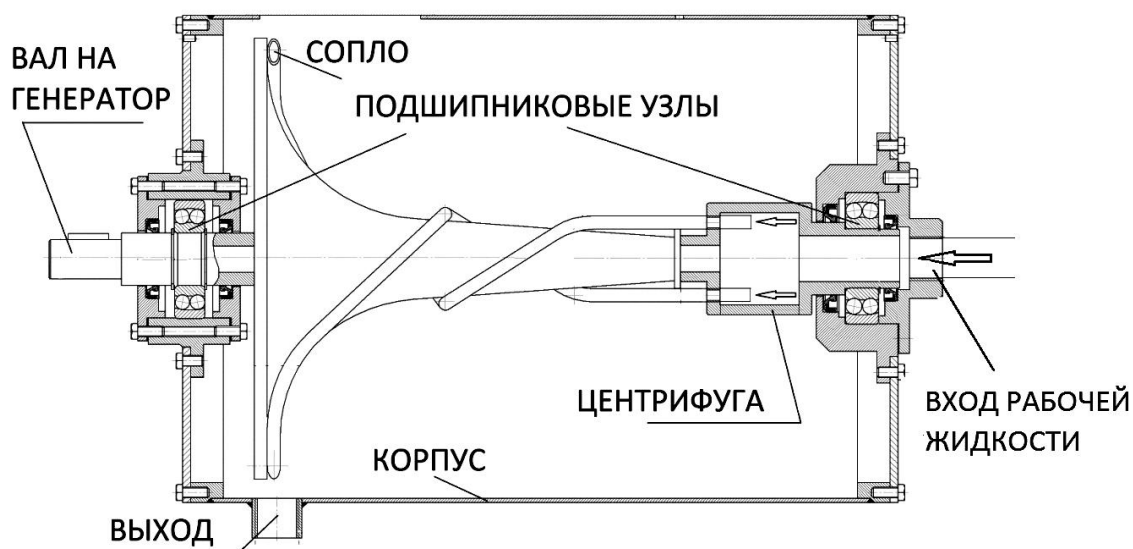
Эскиз предлагаемой конструкции центробежно-вихревого преобразователя.
